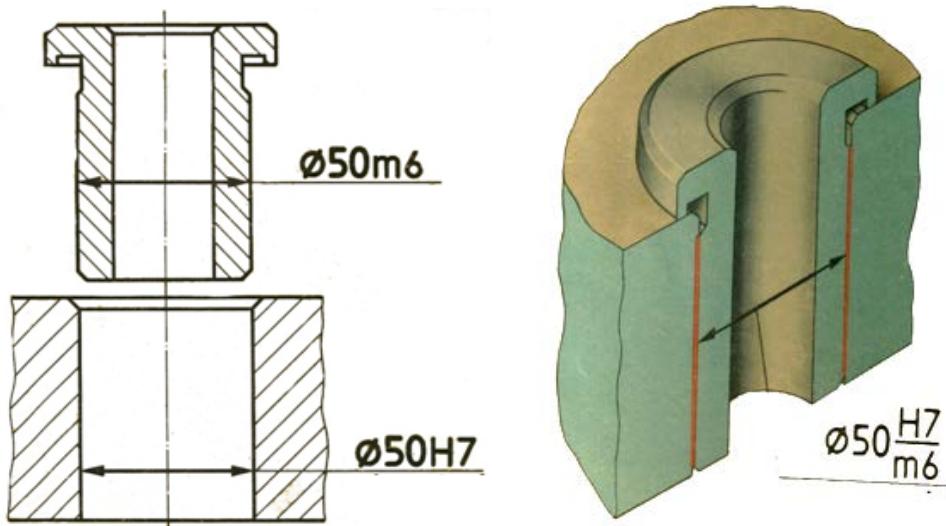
Втулка в крышке кондуктора, точность высокая, нагрузка односторонняя, сборка запрессовкой
